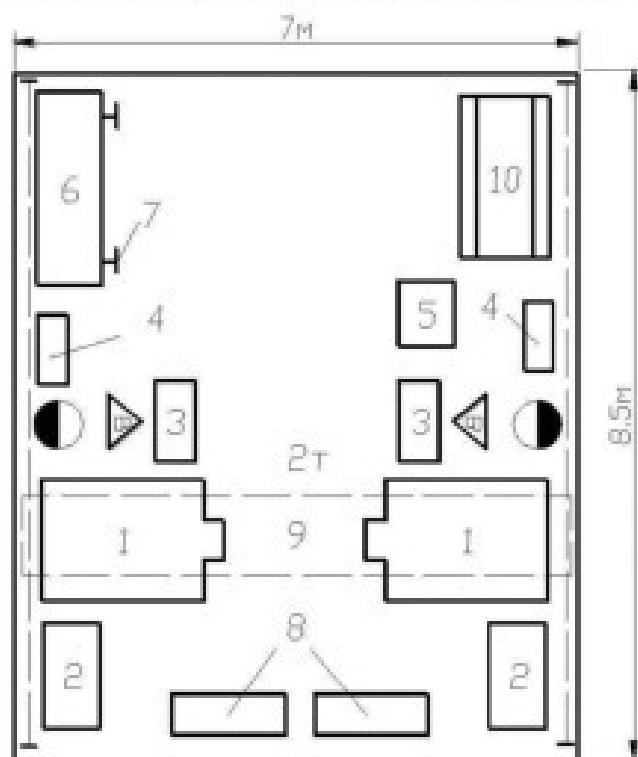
Планировка участка испытаний и доукомплектовки.
